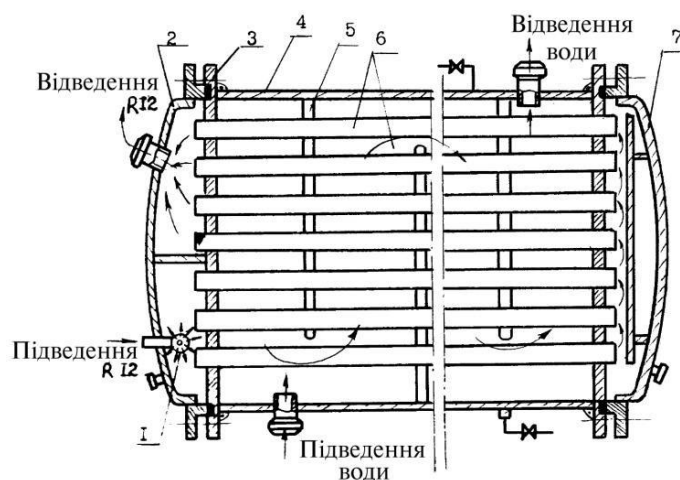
Схема фреонового випарника типу ИТ із внутрішнім кипінням R-12: 1- форсунка; 2- кришка; 3- трубні решітки; 4- обечайка; 5- перегородки; 6- мідні трубки; 7- кришка
